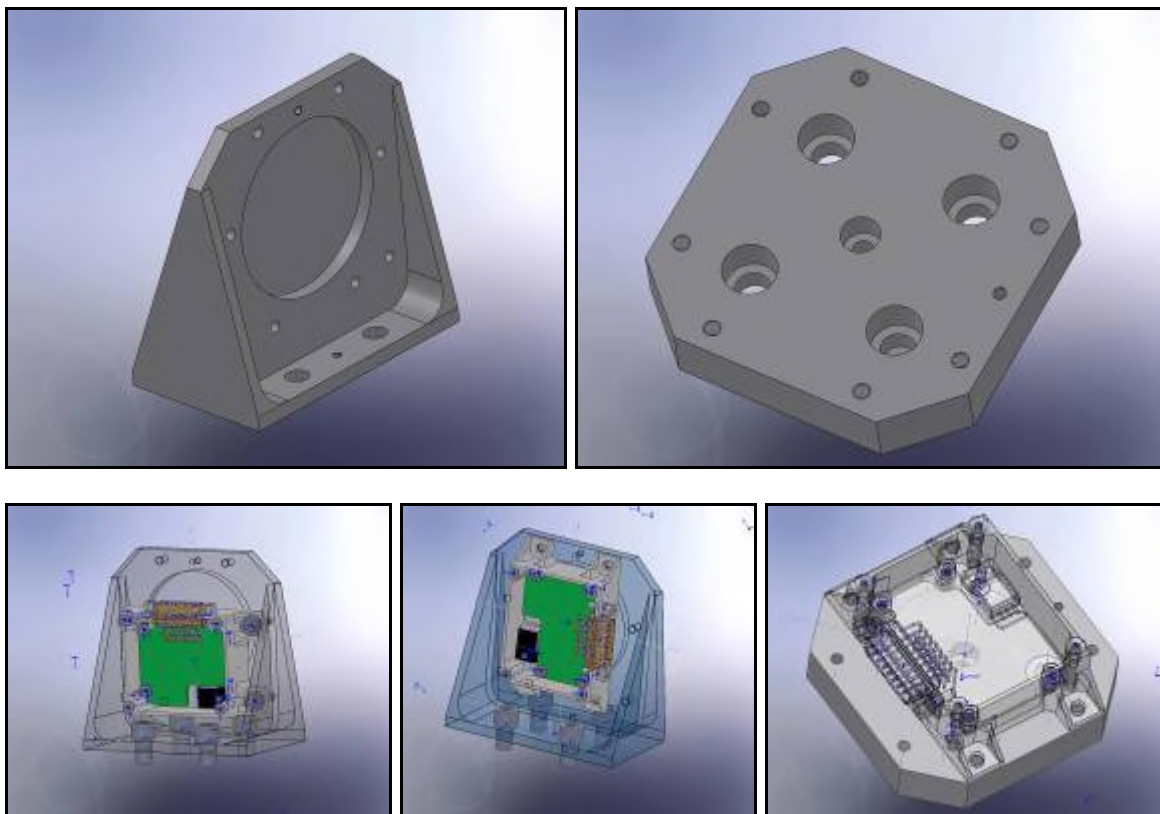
Konstruktion der Montageadapter für die Vibrationstests
